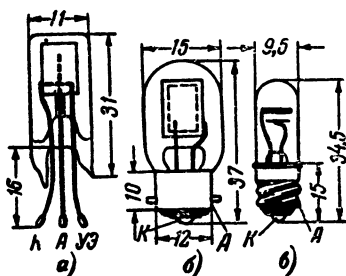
Внешний вид газоразрядных приборов и их цоколевка.
